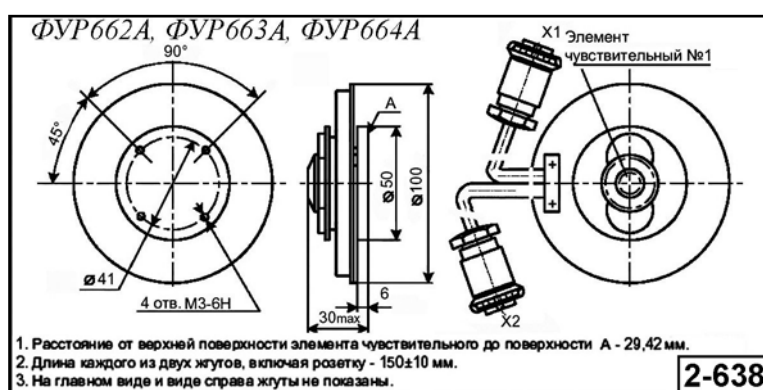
Внешний вид и габаритные размеры ФУР662А, ФУР663А, ФУР664А
